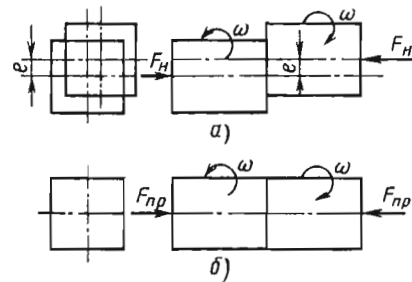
Схема орбитальной сварки трением:
